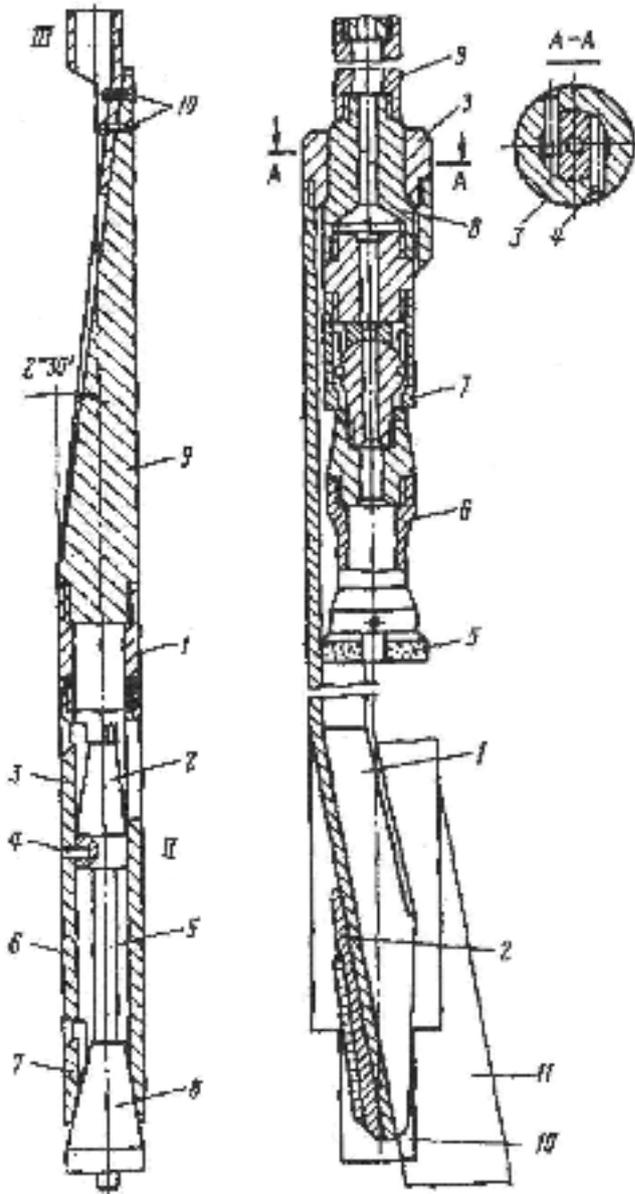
Извлекаемый (стационарный) клин: I – желоб; II – крепежное устройство; III – установочный патрубок; I – удлинитель; 2, 8 – верхний и нижний распорные конусы; 3, 7 – патрубki; 4 – винт; 5 – шток; 6 – соединительная труба; 9 – желоб; 10 – заклепка
